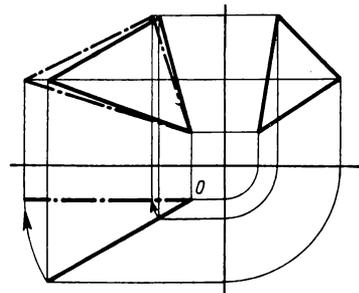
Konstruktion der wahren Größe einer Dreieckfläche
